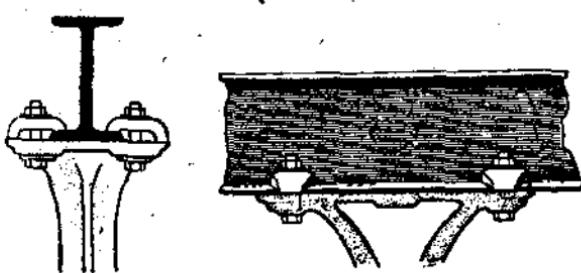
Укрепление подвески на железной балке вдоль балки.
